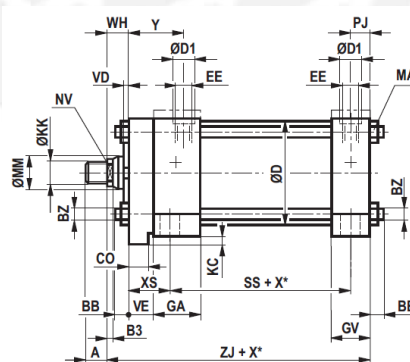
Dimensiones del pistón montaje tipo L (Bosch Rexroth, 2014).
